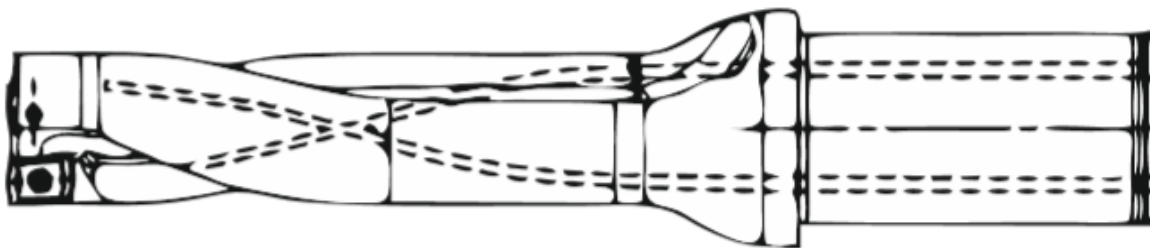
Свердло “CoroDrill DS20” зі змінними пластинами
